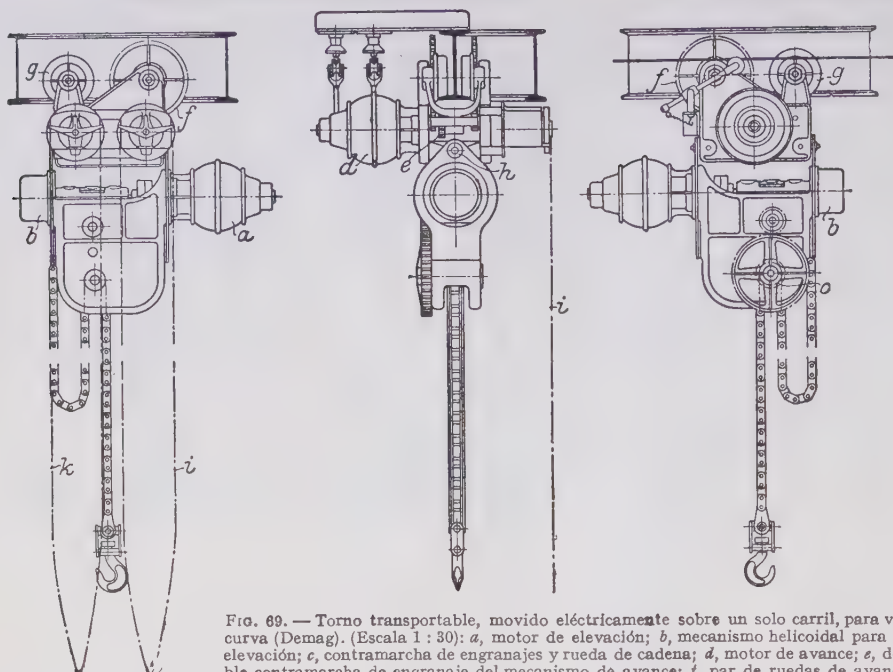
Torno transportable, movido eléctricamente sobre un solo carril, para vía curva (Demag). (Escala 1 : 30): *a*, motor de elevación; *b*, mecanismo helicoidal para la elevación; *c*, contramarcha de engranajes y rueda de cadena; *d*, motor de avance; *e*, doble contramarcha de engranaje del mecanismo de avance; *f*, par de ruedas de avance movidas directamente por el mecanismo; *g*, par de ruedas de avance locas; *h*, eje de giro para el mecanismo de elevación, para la mejor colocación en las curvas; *i*, cadena de mano para el gobierno del mecanismo de elevación; *k*, cadena de mano para el gobierno del mecanismo de avance
